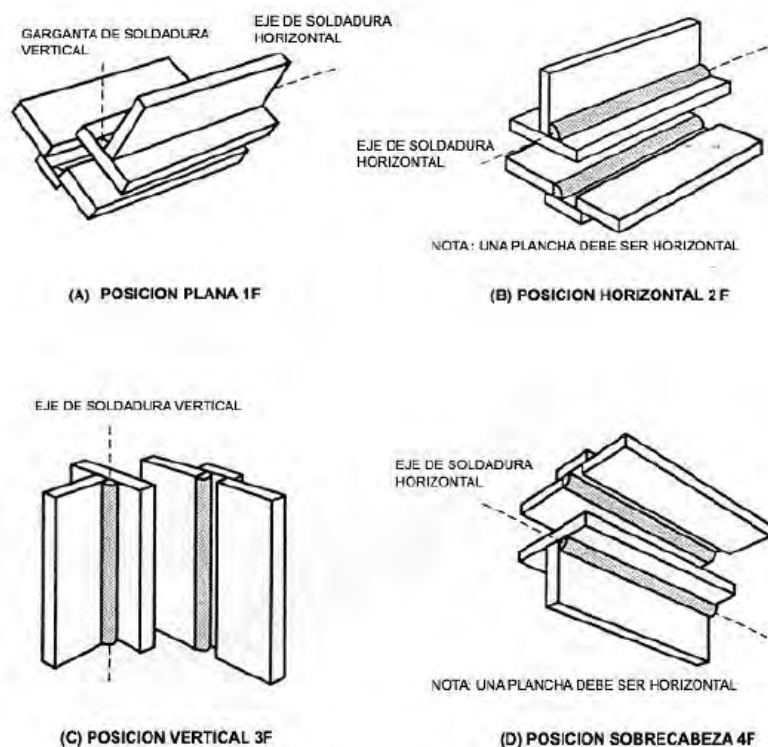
Posiciones de Plancha de Ensayo para Soldaduras de Filete (ver 4.2.4)
